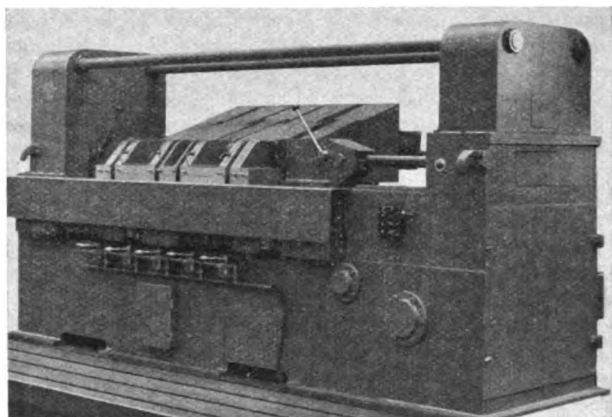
Gesamtansicht der Hinterrohr-Schweißmaschine.
